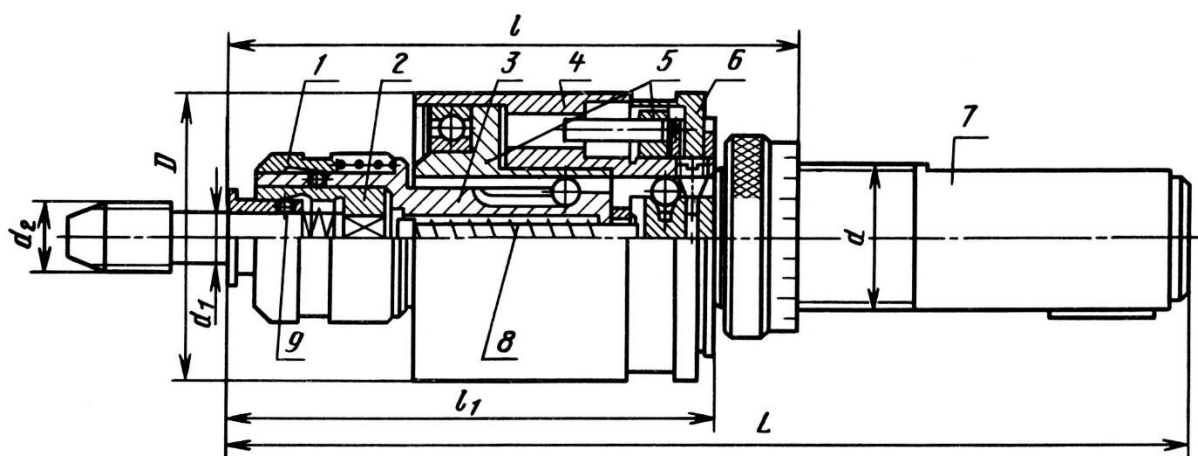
Регулируемый резьбонарезной патрон с предохранительным устройством для нарезания резьбы метчиками М6...М16
